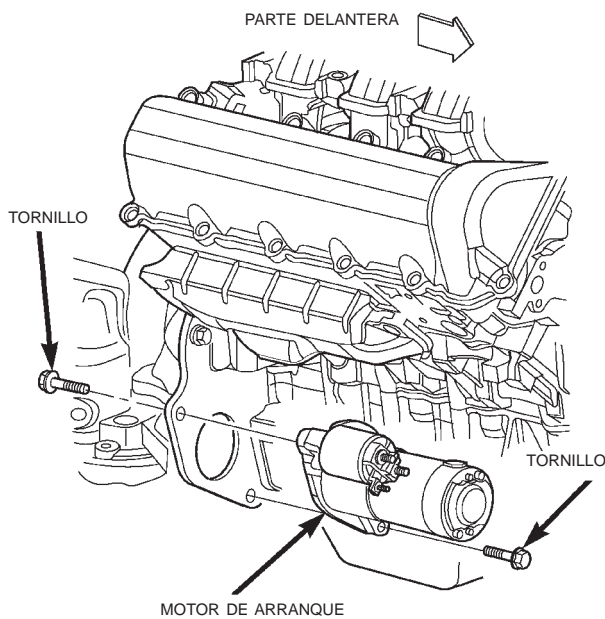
Desmontaje e instalación del motor de arranque - Motor 4.7L
